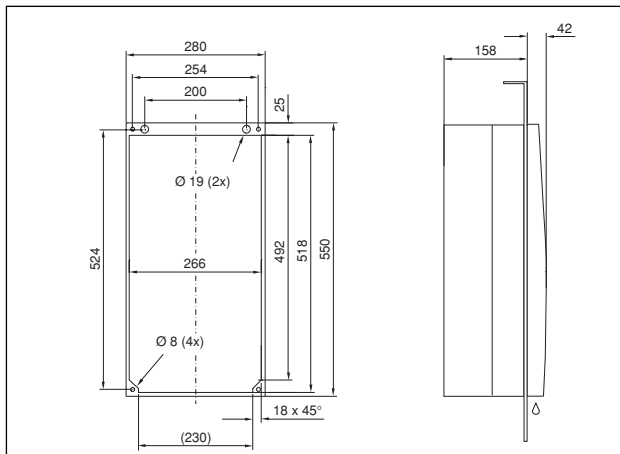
SK 3303.xxx, SK 3361.xxx Komplet inbyggnad
